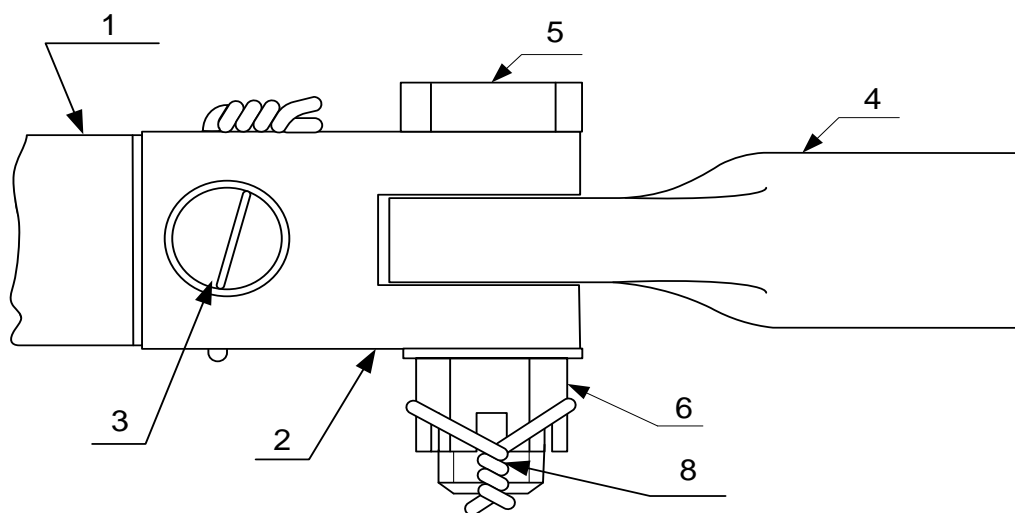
Шарнир шибера электропривода с элементами крепления.
